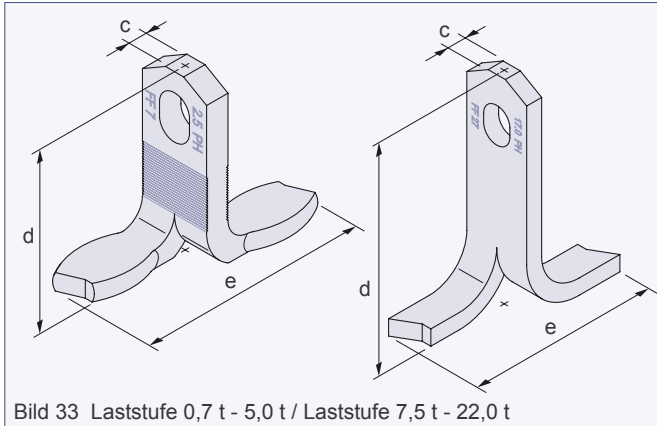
Laststufe 0,7 t - 5,0 t / Laststufe 7,5 t - 22,0 t
